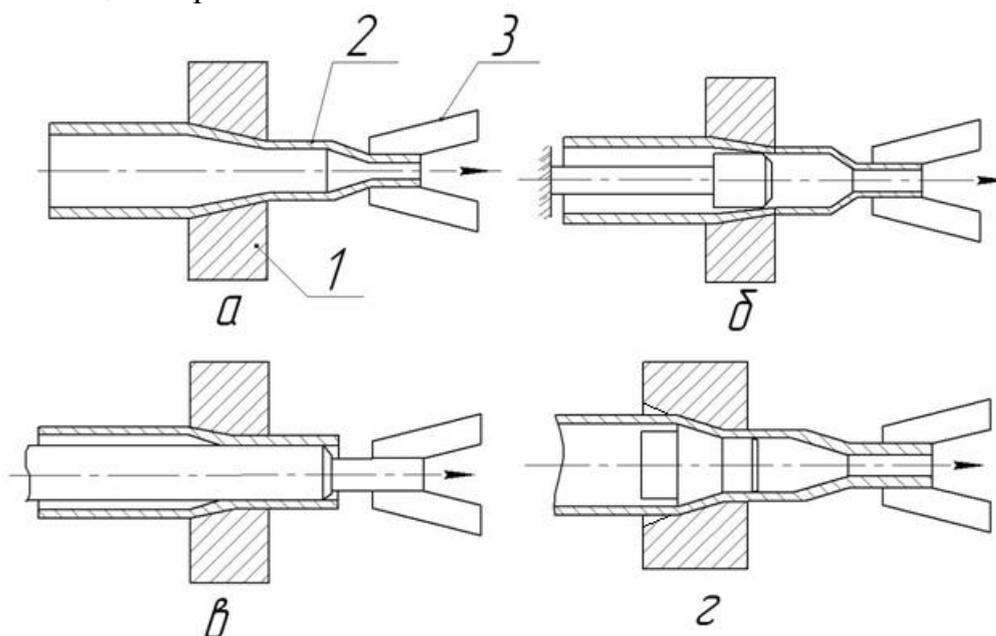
Схема волочения труб: 1—волока; 2—труба; 3—захват.
